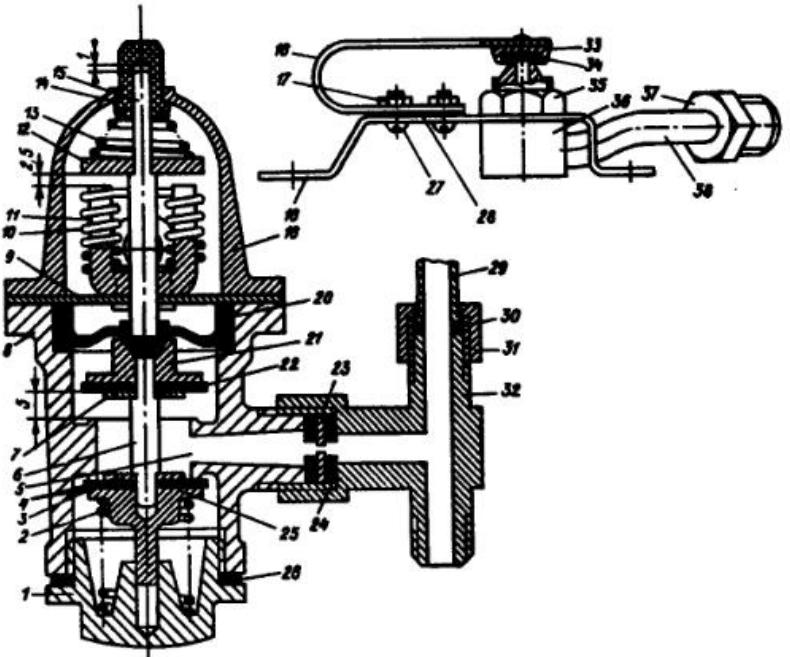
Газовый магнитный клапан с датчиком тяги водонагревателя АГВ-80:
